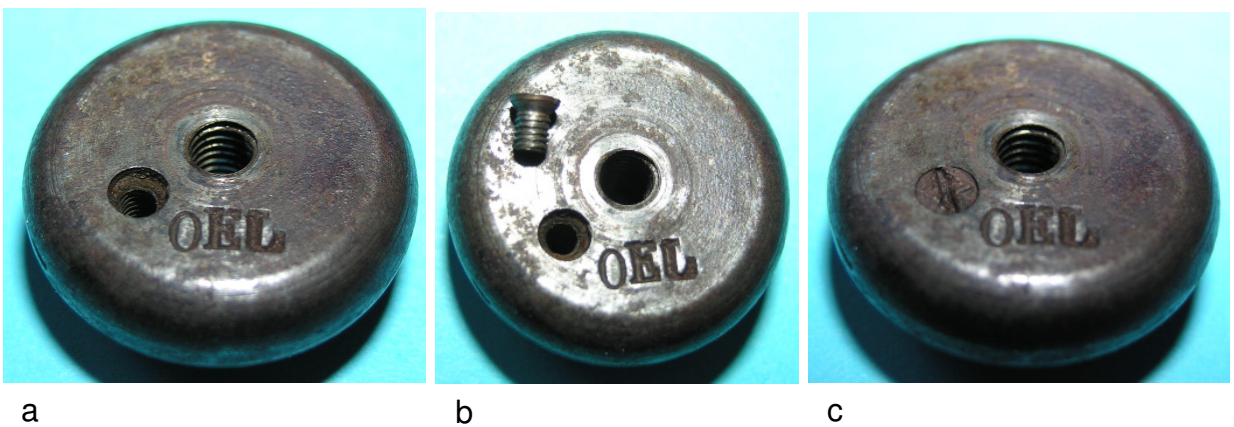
Reibrad: a) Gewindebohrungen im Reibrad, b) Ölbohrung und Öllochverschluss, c) Verschlussene Ölbohrung
